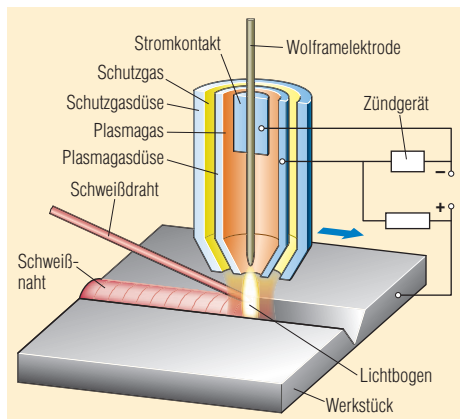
Prinzip des Plasmaschweißens.
